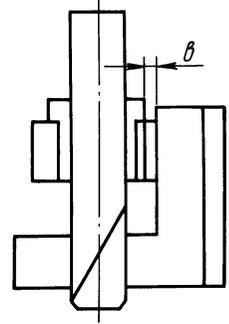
К проверке размещения кондукторной втулки относительно обрабатываемой детали.
